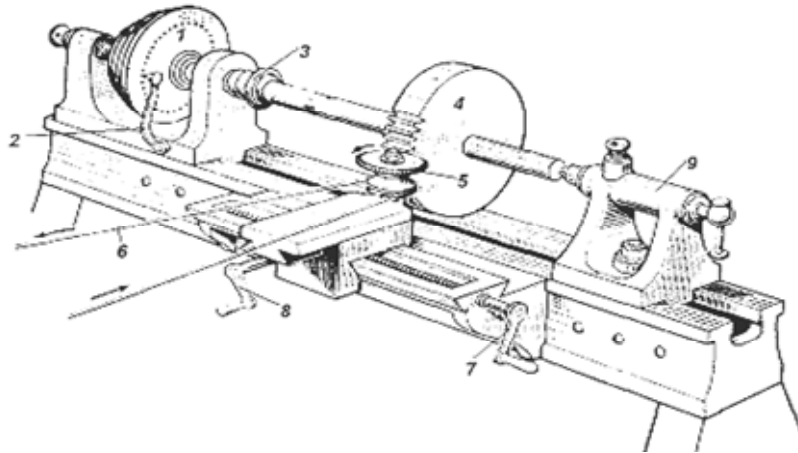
Схема немеханизированного суппорта и делительного устройства зубофрезерного станка (рисунок Дж. Несмита, 1841 г.):
